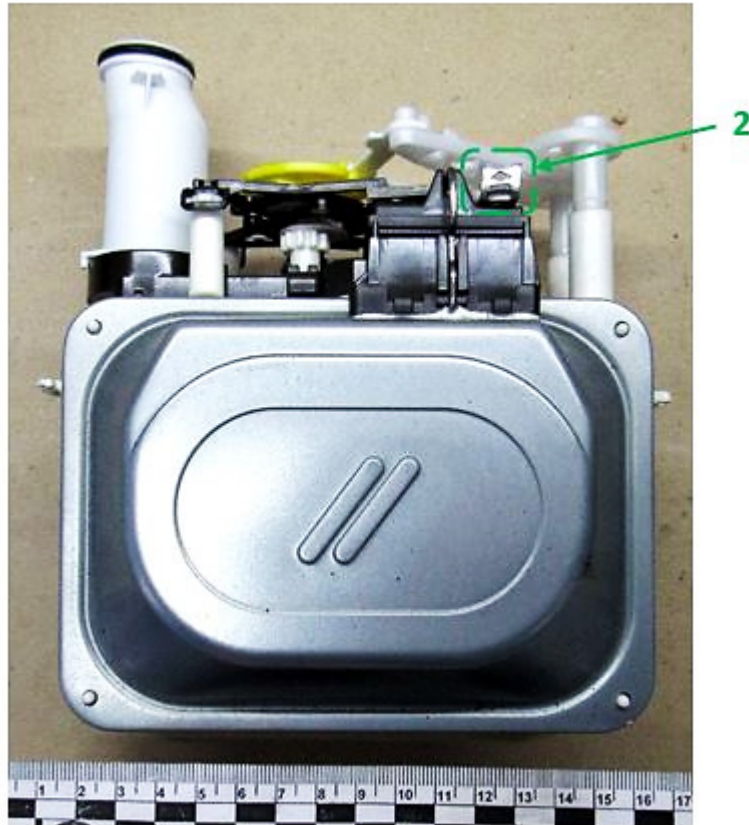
Загальний вигляд внутрішніх поверхонь та механізмів лічильника газу «Ельстер G4» і місце розташування металевої пластини з нашаруванням полімерної речовини чорного кольору (вигляд збоку)
